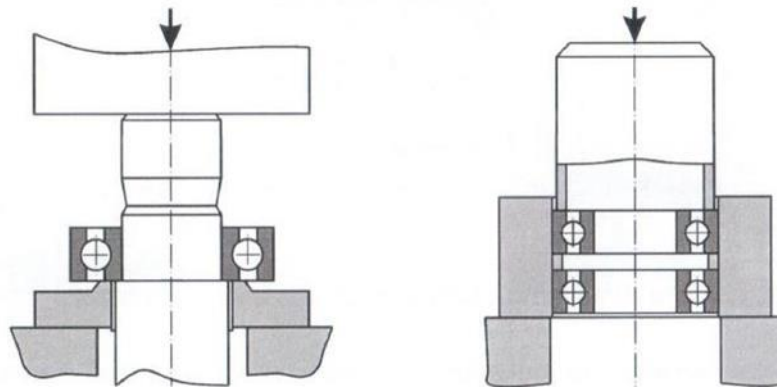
Знімання підшипників, встановлених на вал або в корпус з натягом
